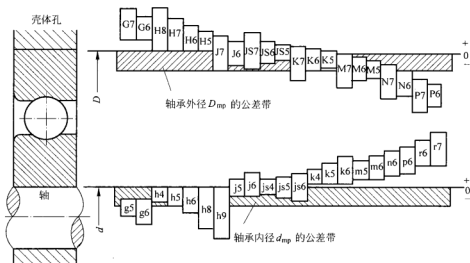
滚动轴承与轴、外壳孔配合的公差带图
